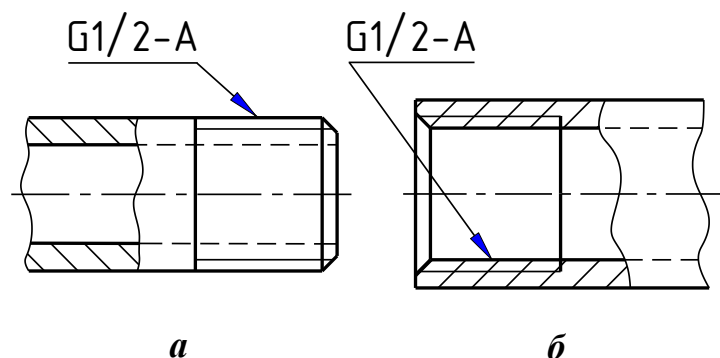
Обозначение трубной цилиндрической резьбы, нанесение ее размера:
